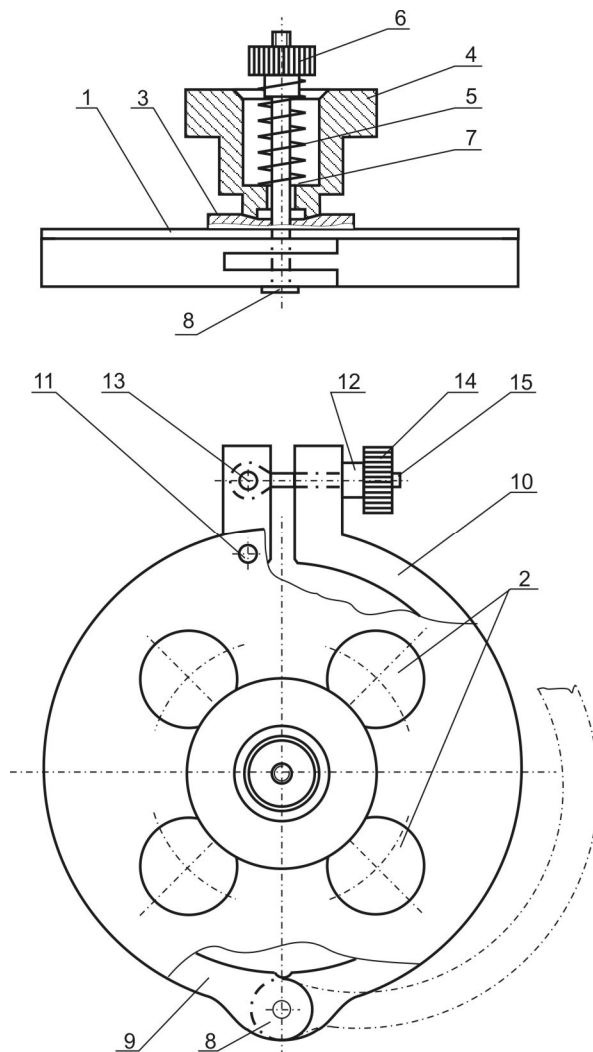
Пристрій для підготовки до контролю ступеня безпеки закупорювання.
